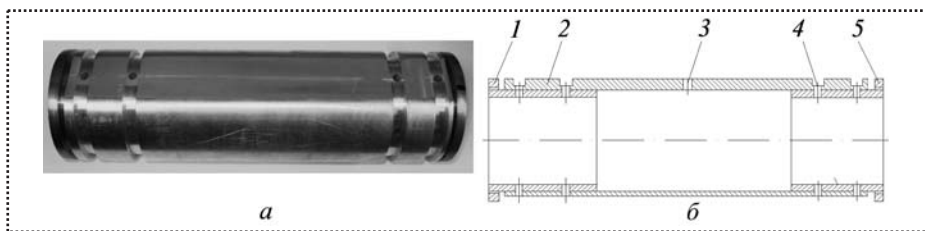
Общий вид (а) и конструкция (б) подшипникового узла
